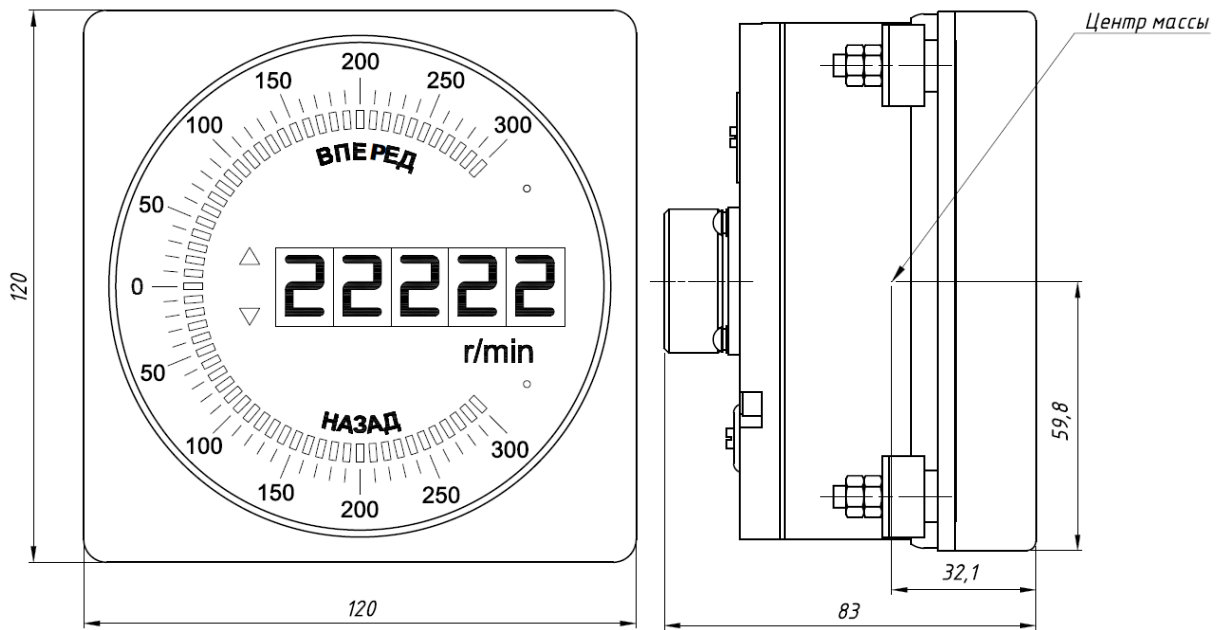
Габаритный чертеж блока индикации МТК–БИ
